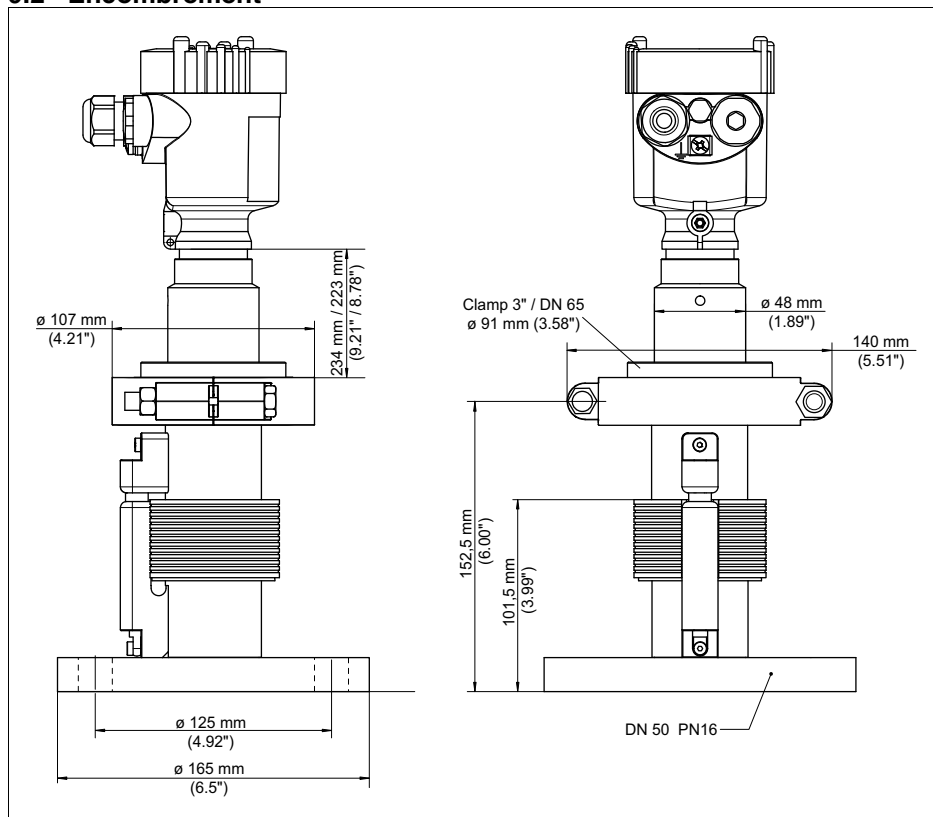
Dimensions de la fermeture rapide et pivotante pour VEGAPULS 66.
